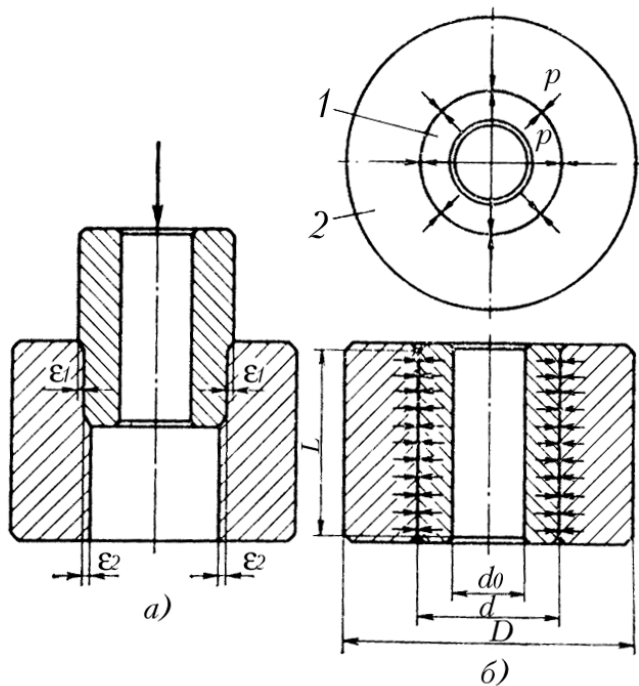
Схема запрессовки (а) и схема прессового соединения – натяг охватываемой детали 1; – натяг охватывающей детали 2.
